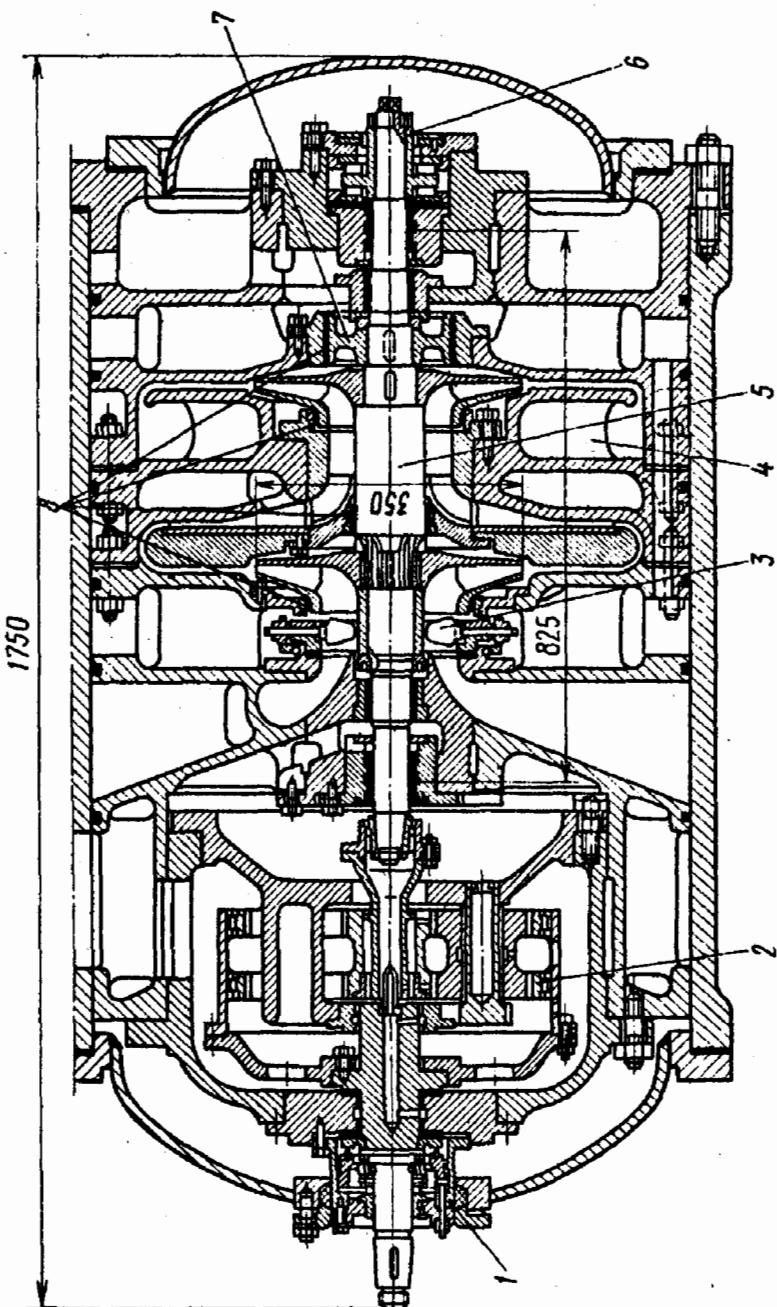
Двухступенчатый центробежный фреоновый хладильный компрессор:
